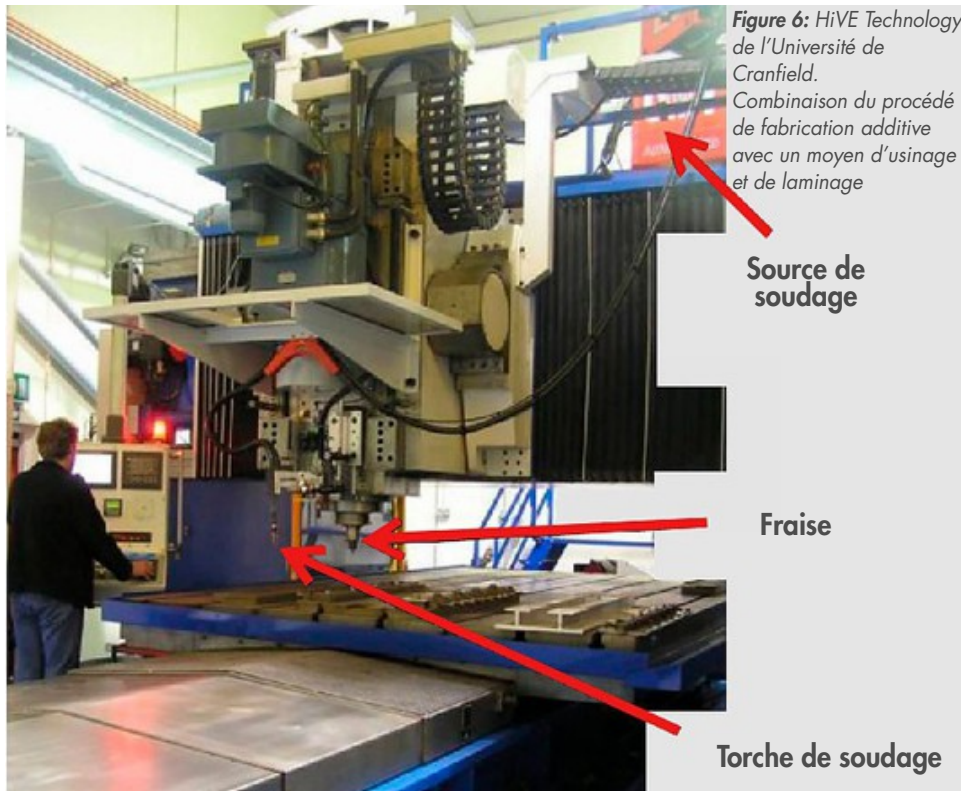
HiVE Technology de l'Université de Cranfield. Combinaison du procédé de fabrication additive avec un moyen d'usinage et de laminage
